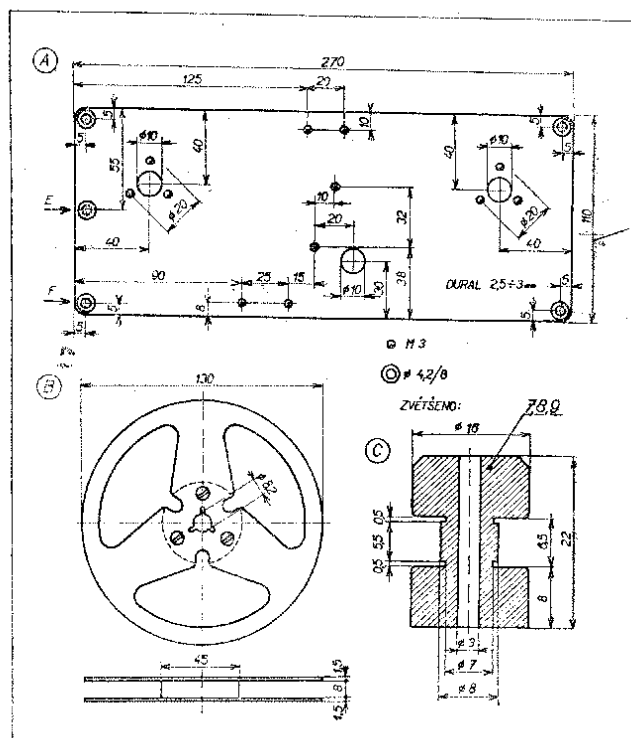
je detail navíjecí kladky, která je spojena s hlavní kladkou gumovým řemínkem (průměr asi 3 mm), který koupíme v prodejních s gumovým zboží (těsnicí kroužky). Cívka s páskem pouze leží na kotoučku a pohybuje se jen třením (na rozdíl od převíjecí kladky, kde je cívka našroubována kolíčkem). Pro zlepšení tření (a omezení hlu-
